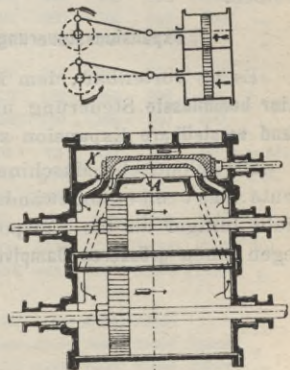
1694. Gleichgerichtete Kolbenbewegung.
